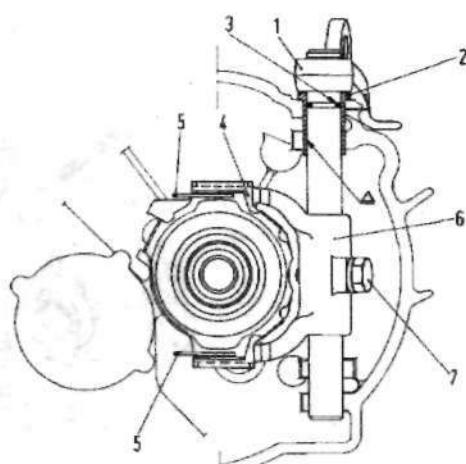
Детали механизма высвобождения сцепления (Раздел 4)
